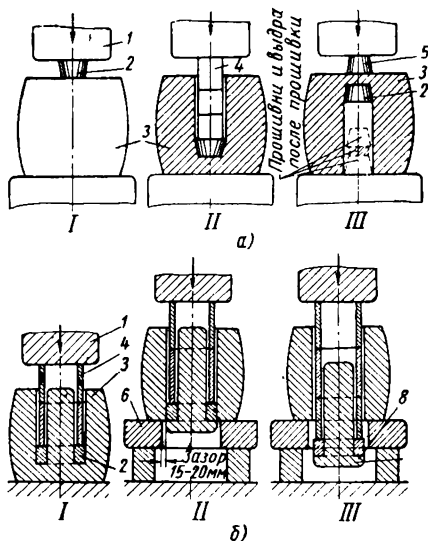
Очередность переходов I, II, III при прошивке: а — сплошным прошивнем; б — пустотелым прошивнем; 1 — верхний боек; 2 — прошивень; 3 — прибыльная часть слитка; 4 — надставка; 5 — второй прошивень; 6 — кольцо
